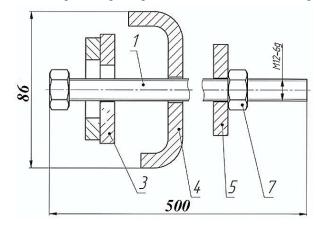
Болт из набора «СНКЛ-3 ССД» с крепёжными деталями: 1 – болт; 3 – накладка; 4 – швеллер; 5 – шайба; 7 – гайка М12.
